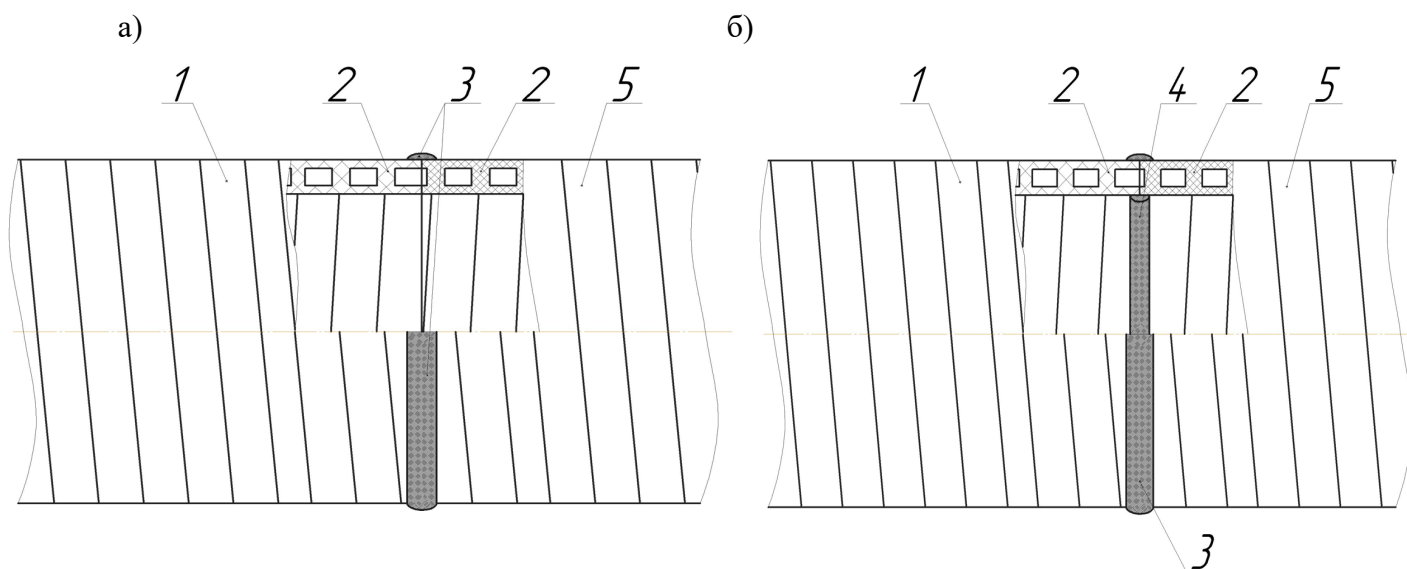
Соединение труб POLYCORR SVT экструзионной сваркой:
